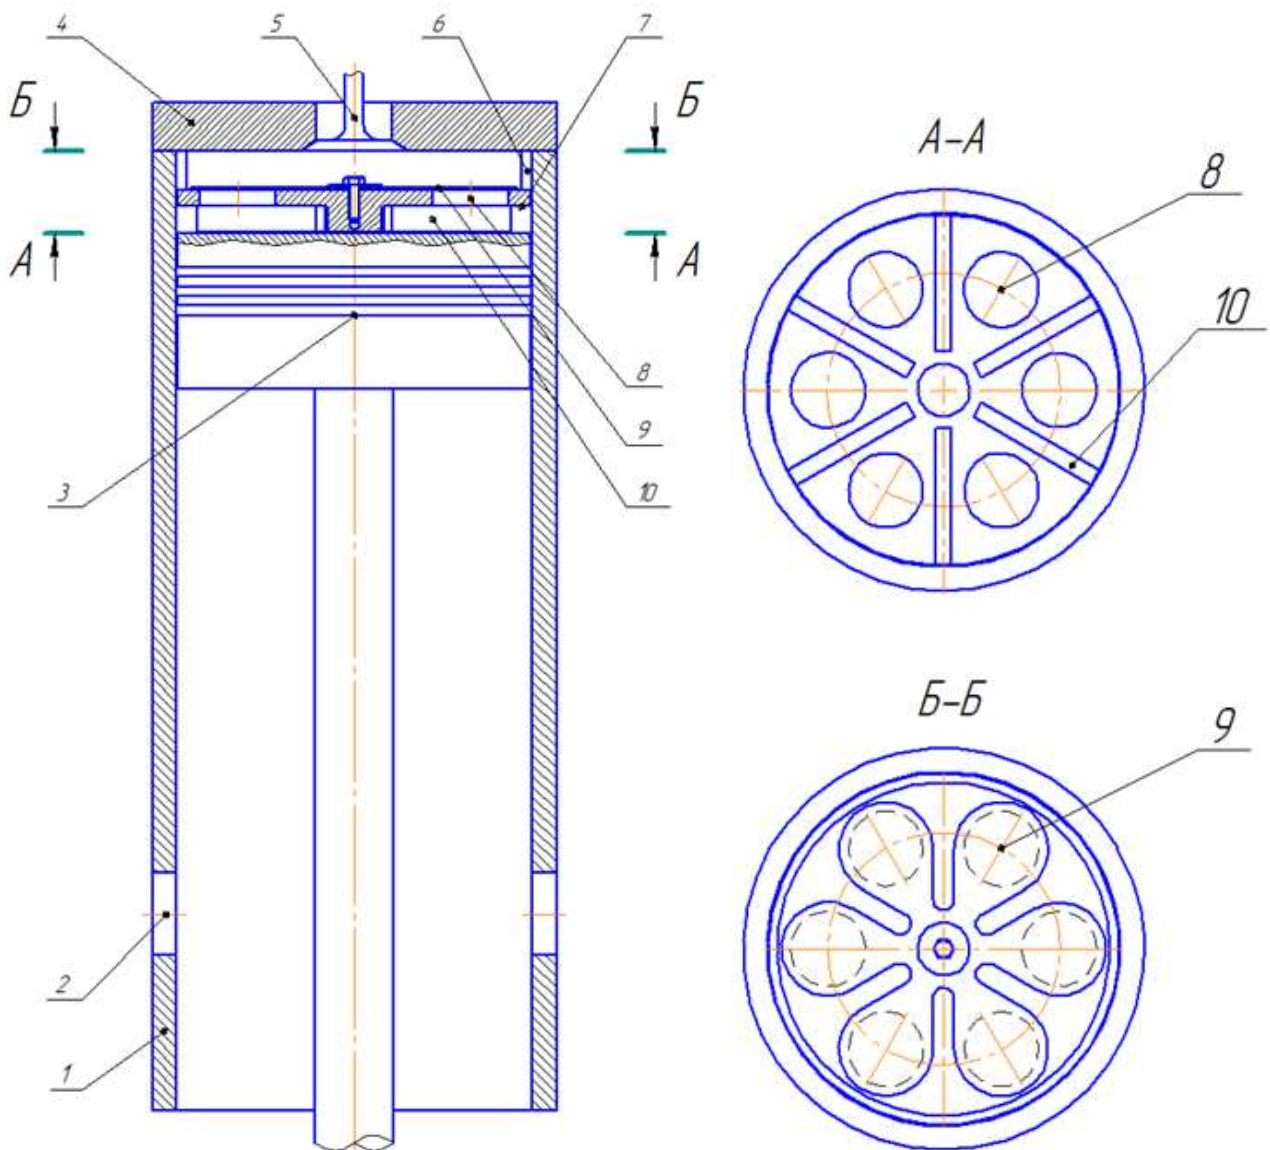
Положення поршня і газового поршня у верхній мертвій точці: 1 – циліндрова втулка; 2 – продувні вікна; 3 – поршень; 4 – кришкою циліндра; 5 – випускний клапан; 6 – дистанційне кільце; 7 – газовий поршень; 8 – повітряні отвори; 9 – клапани; 10 – ребра жорсткості
